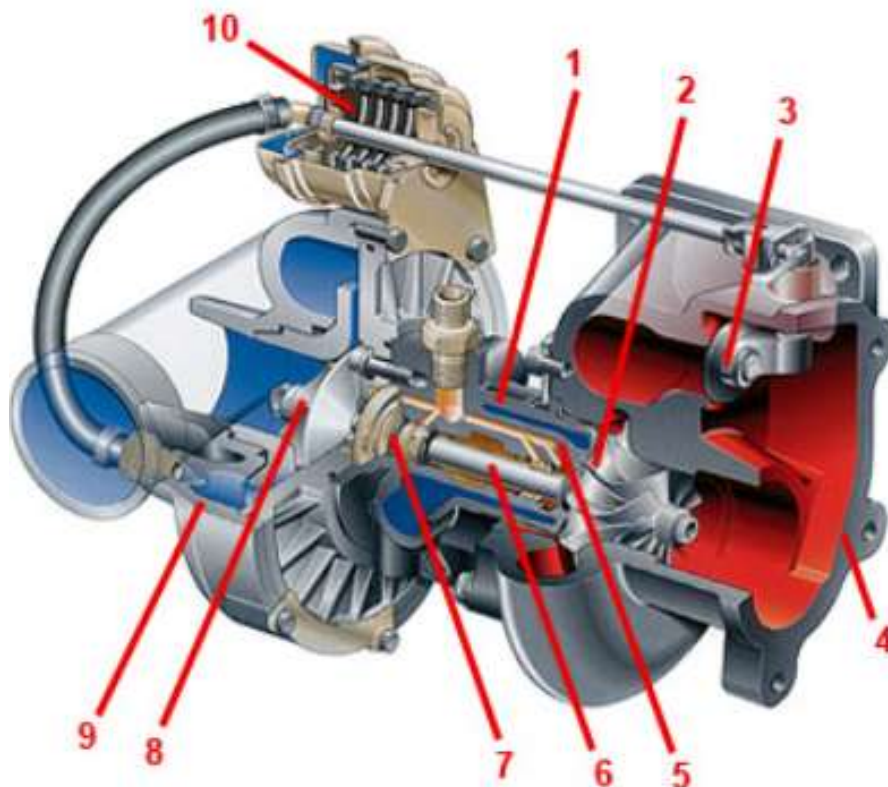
Пристрій турбокомпресора: 1 — корпус підшипників; 2 — турбінне колесо; 3 — перепускний клапан; 4 — корпус турбіни; 5 — масляні канали; 6 — вал ротора; 7 — підшипник ковзання;
